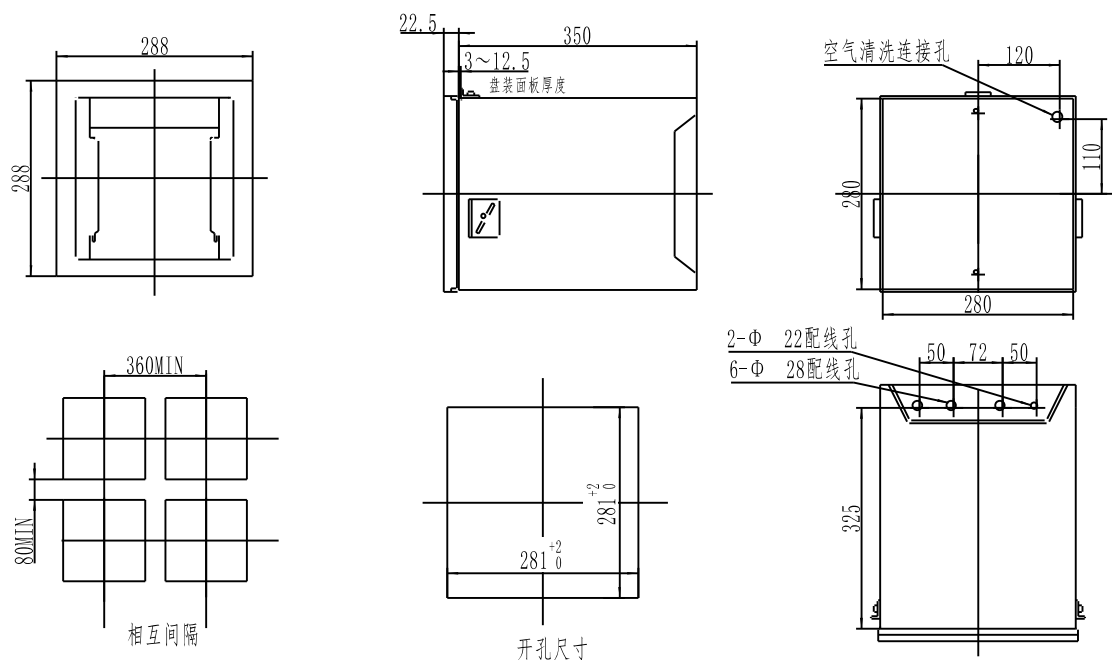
FR18000 外形尺寸及仪表盘尺寸 (单位: mm)
